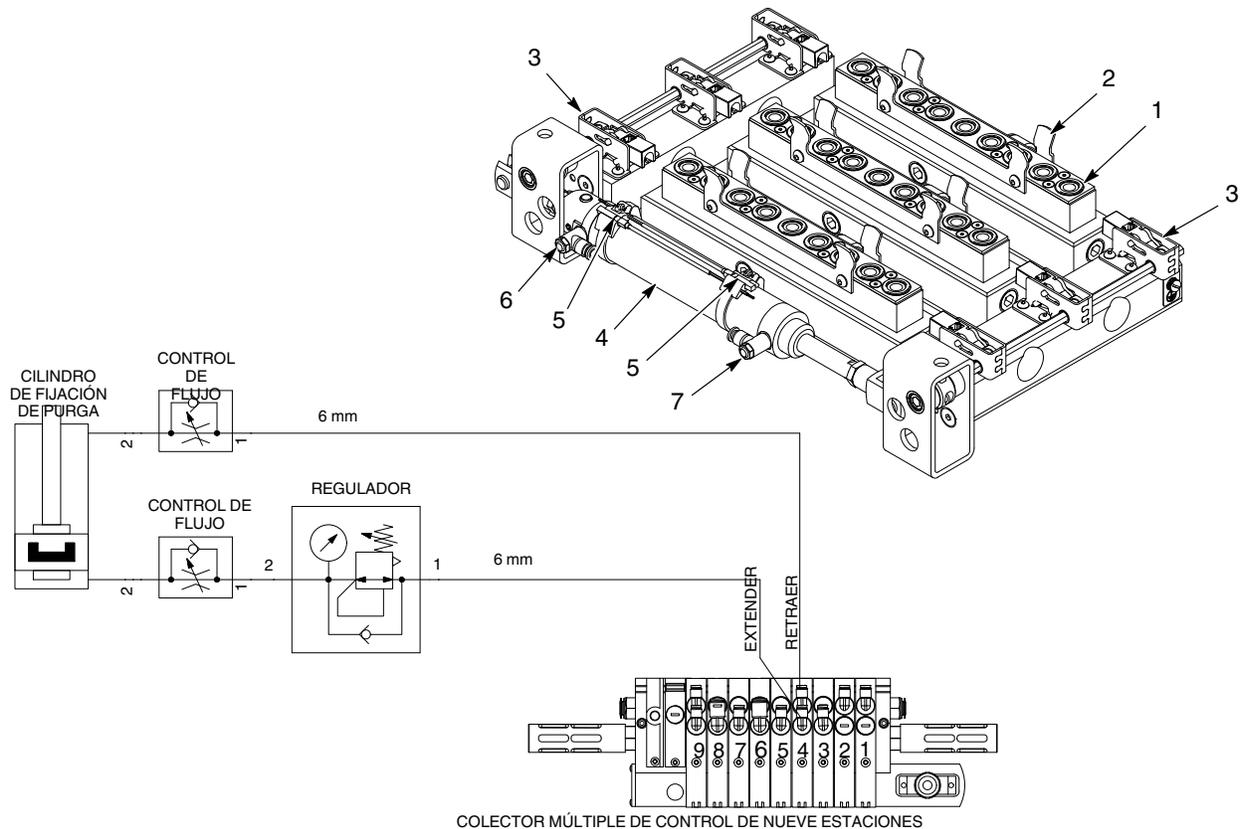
Conjunto del distribuidor de purga (se muestra el conjunto de 3 lanzas con el cilindro y los latiguillos en la posición de fijación)
